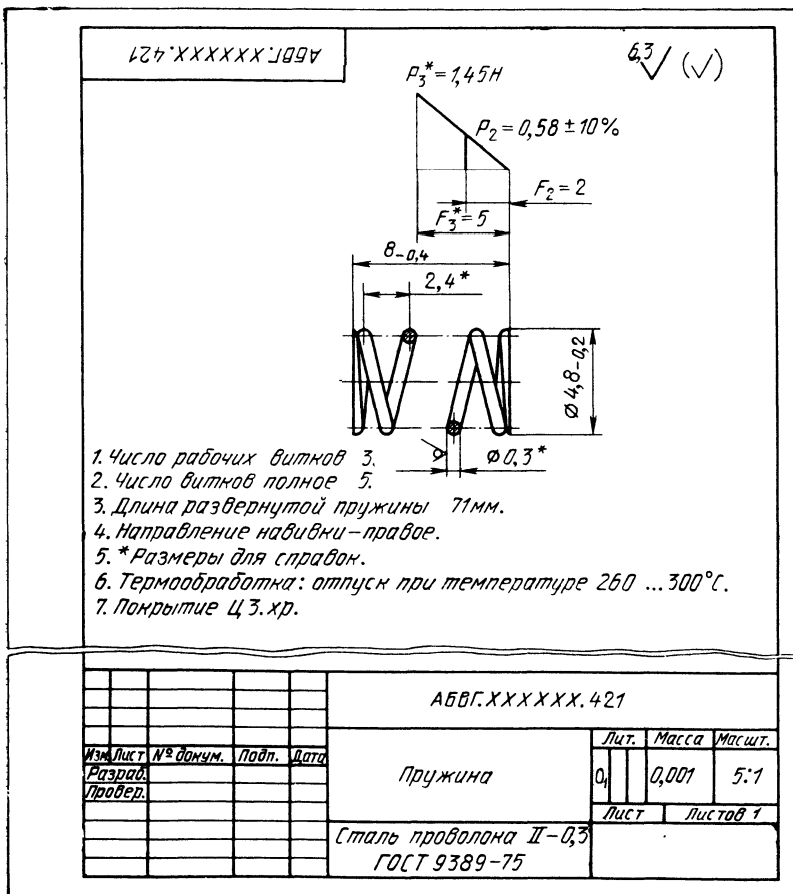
Рабочий чертеж винтовой пружины сжатия
